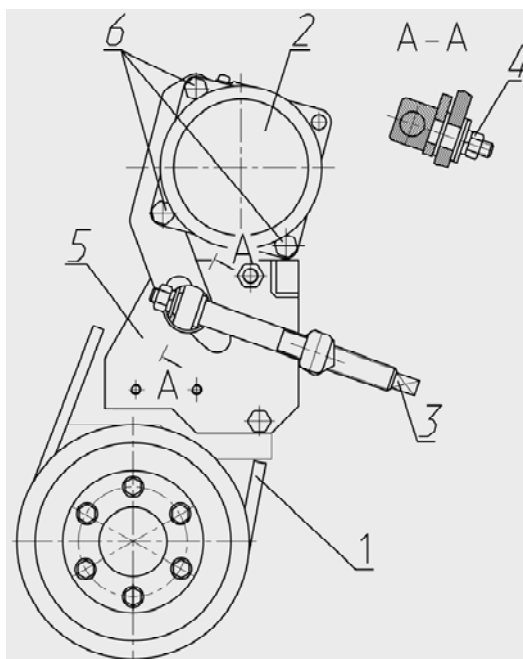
Привод компрессора кондиционера на тракторах «БЕЛАРУС 2522.1/2522ДВ/3022ДВ/3022.1» (с двигателем ДТА 530 Е).
